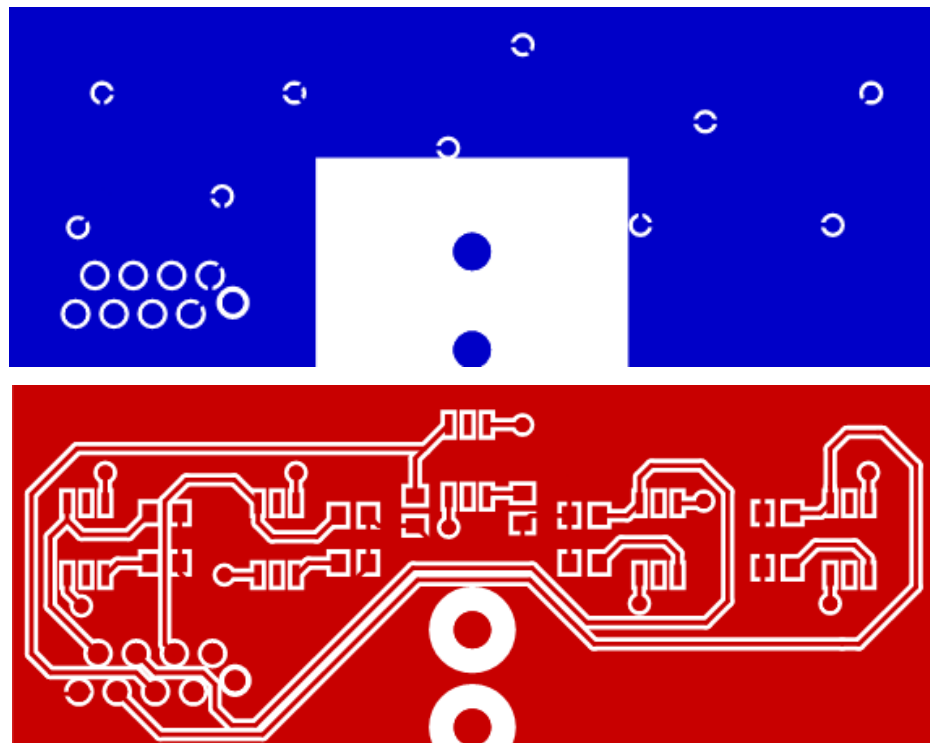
Linienboard 5Sensor - Platine - Top & Bottom
